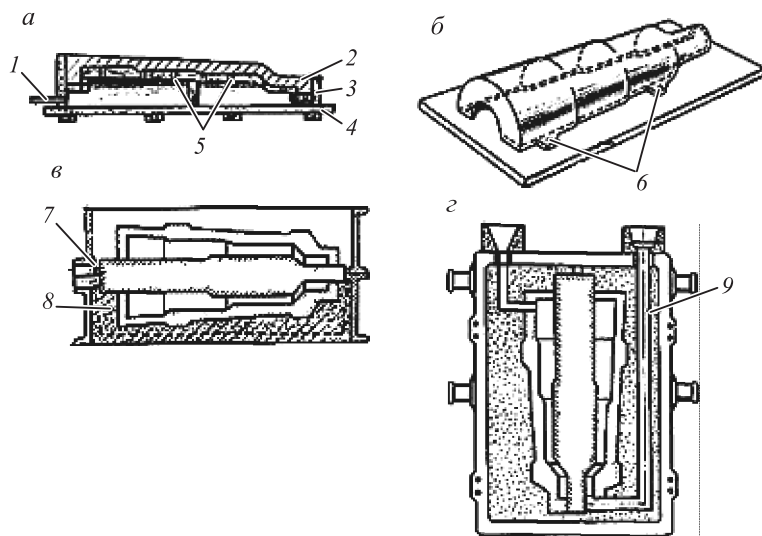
Технология ручного изготовления форм из химически твердеющих оболочек: *а* – изготовление оболочки; *б* – оболочка, снятая с модели; *в* – положение перед набивкой верхней опоки; *г* – форма, подготовленная к заливке; 1 – стучер; 2 – нижняя оболочка; 3 – рамка; 4 – модельная плита; 5 – отверстия; 6 – отверстия в выступах оболочки; 7 – стержень; 8 – нижняя полуформа; 9 – керамика для выполнения литниковой системы
